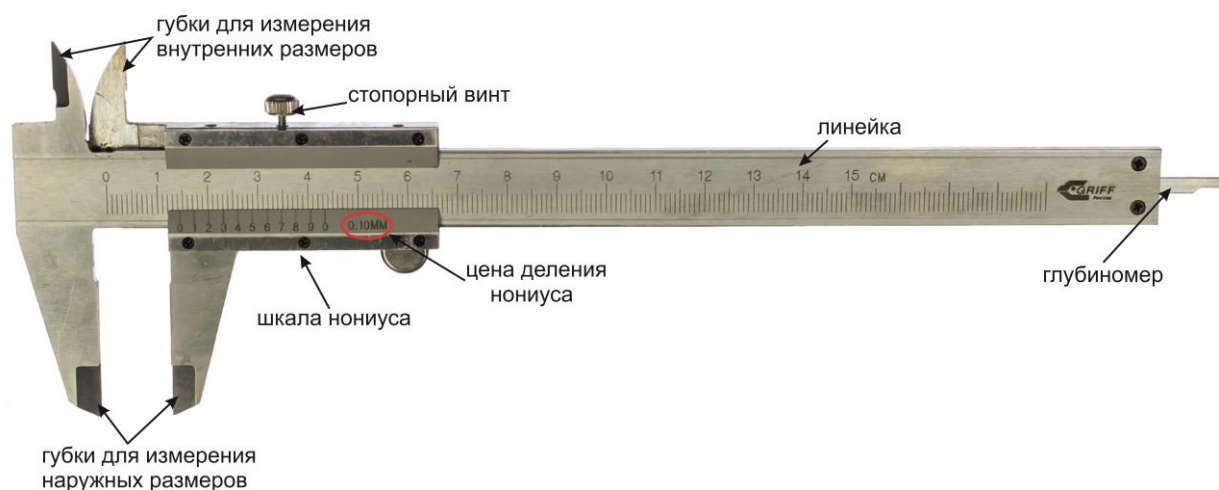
Внешний вид и основные элементы штангенциркуля
